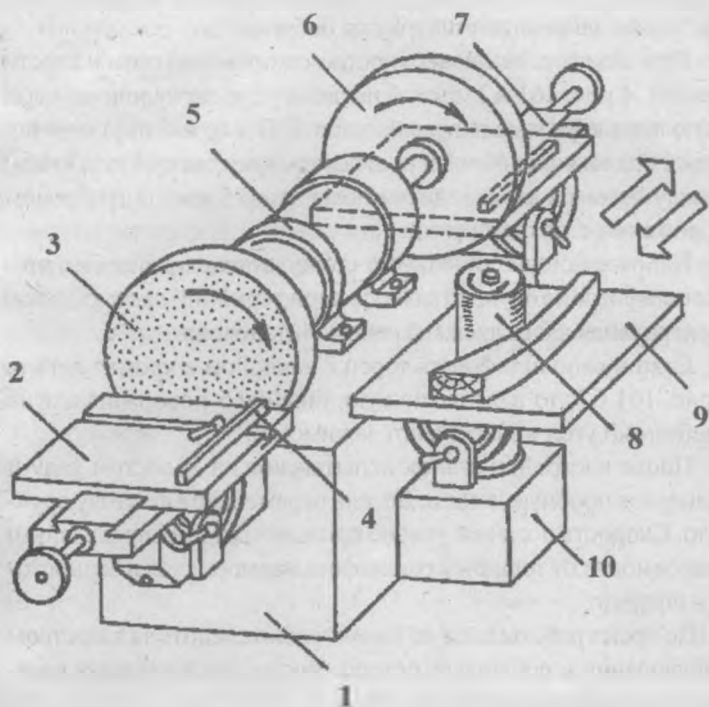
Комбинированный шлифовальный станок с двумя дисками и бобиной ШЛДБ-4:
